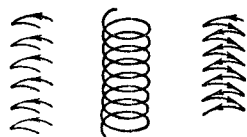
Техника управления горелкой и прутком при газовой сварке
